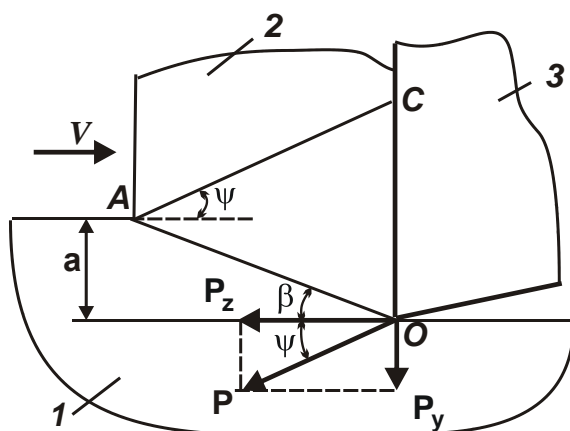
Расчетная схема параметров стружкообразования при резании: 1 – обрабатываемый материал; 2 – образующаяся стружка; 3 – режущий инструмент
